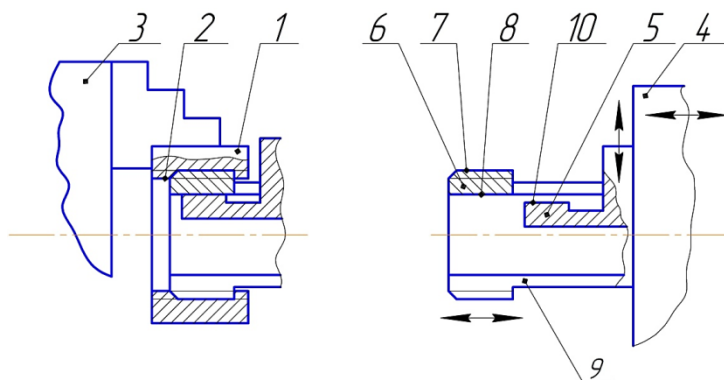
Схема способа переустановки детали с резьбовым отверстием
